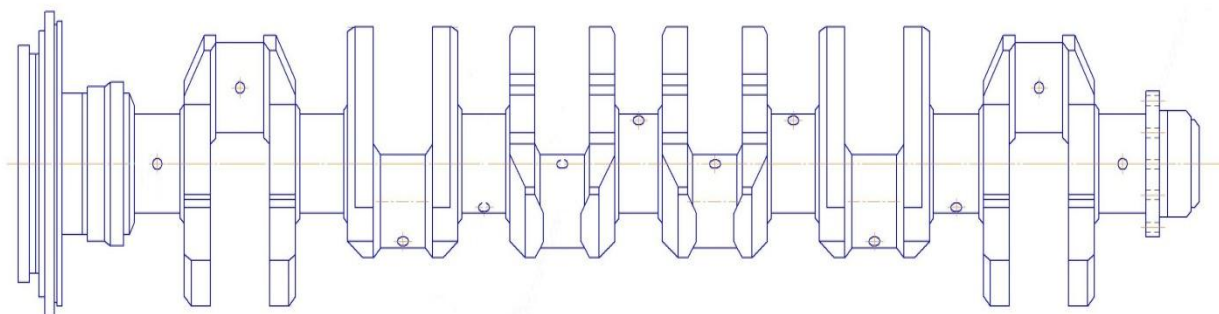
Эскиз заготовки, подвергаемой термической обработке
